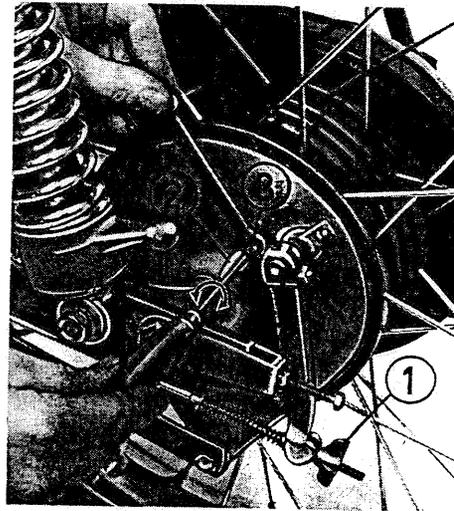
Régler le frein de roue arrière et le contacteur de stop
